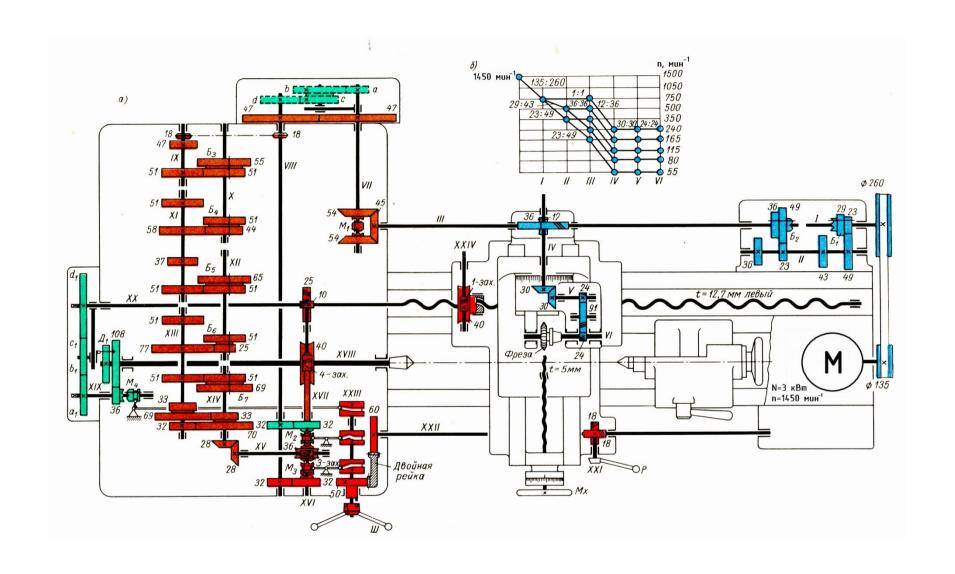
Кинематическая схема резьбофрезерного станка модели 561
